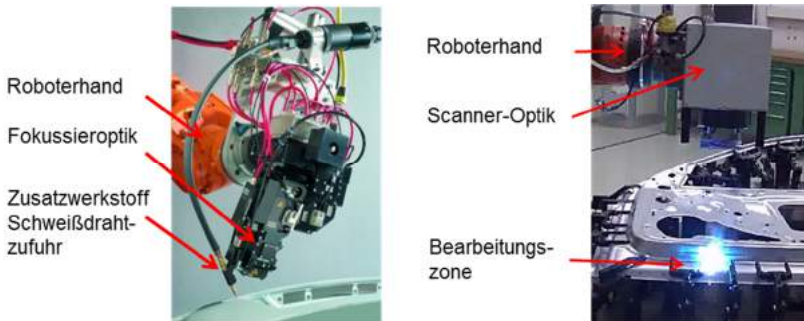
Links: Taktill geführtes Laserstrahlschweißen mit Zusatzwerkstoff [13].
